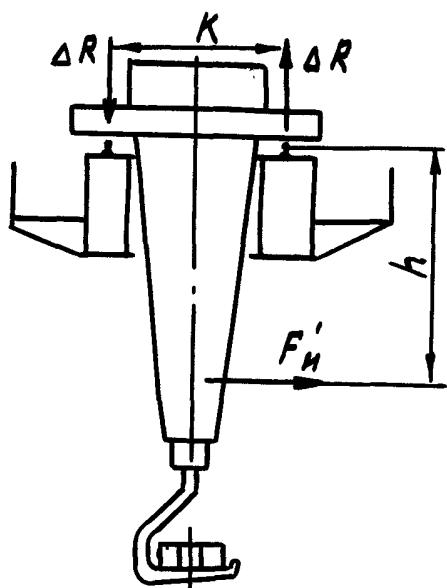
Схема к расчету устойчивости тележки мостового крана
